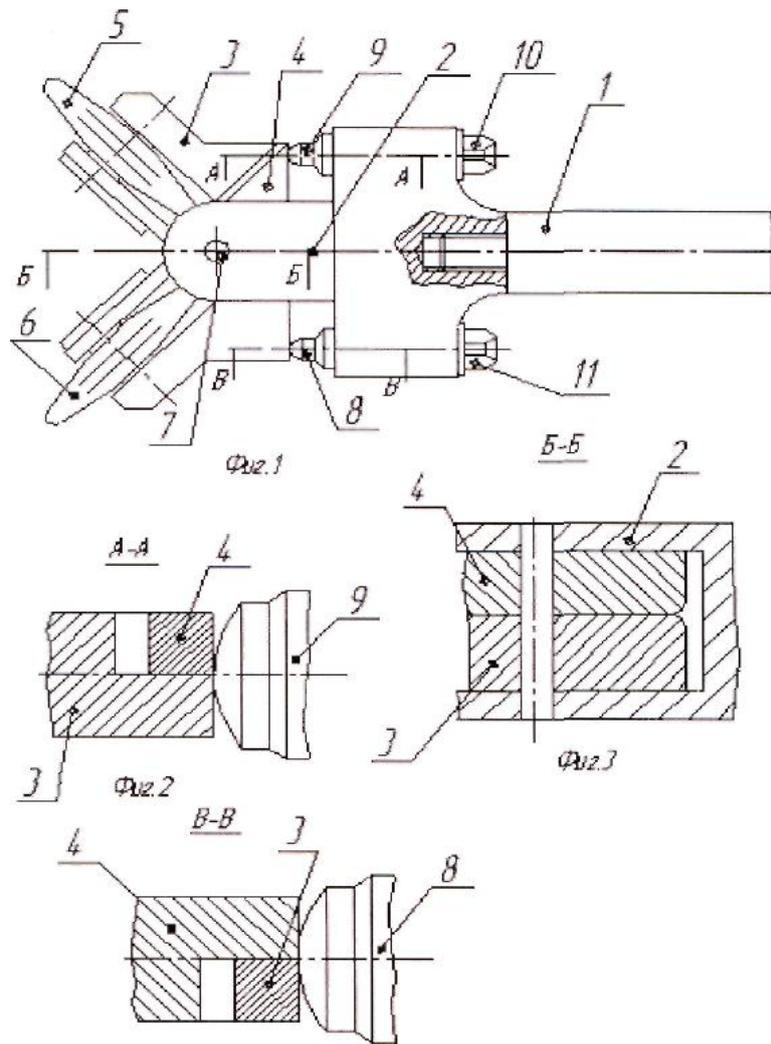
Устройство для чистовой и упрочняющей обработки поверхностей деталей
